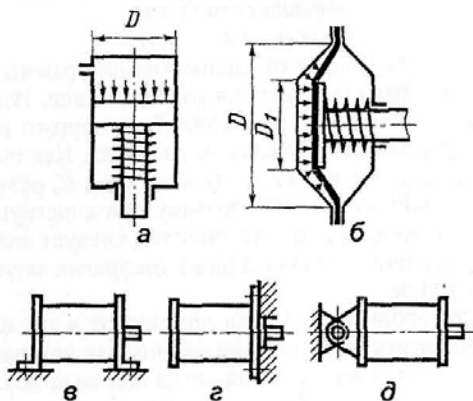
Схемы пневмодвигателей одностороннего действия и способы крепления их на корпус.
